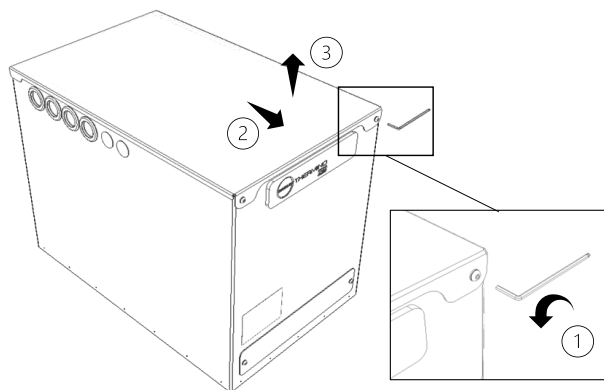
Retrait du couvercle de la batterie thermique Thermino
